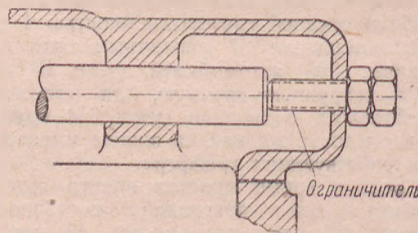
Ограничитель хода валика четвертой и пятой передач коробки перемены передач.
